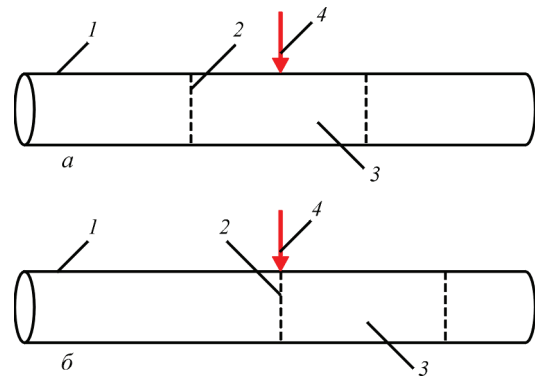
Схема двох типів зразків для проведення дилатометричного дослідження: а — зварний метал у центрі зразку (I тип); б — зона сплавлення у центрі зразку (II тип); 1 — циліндричний металевий зразок; 2 — лінія сплавлення; 3 — зона зварного з'єднання; 4 — місця прилягання щупів дилатометра
